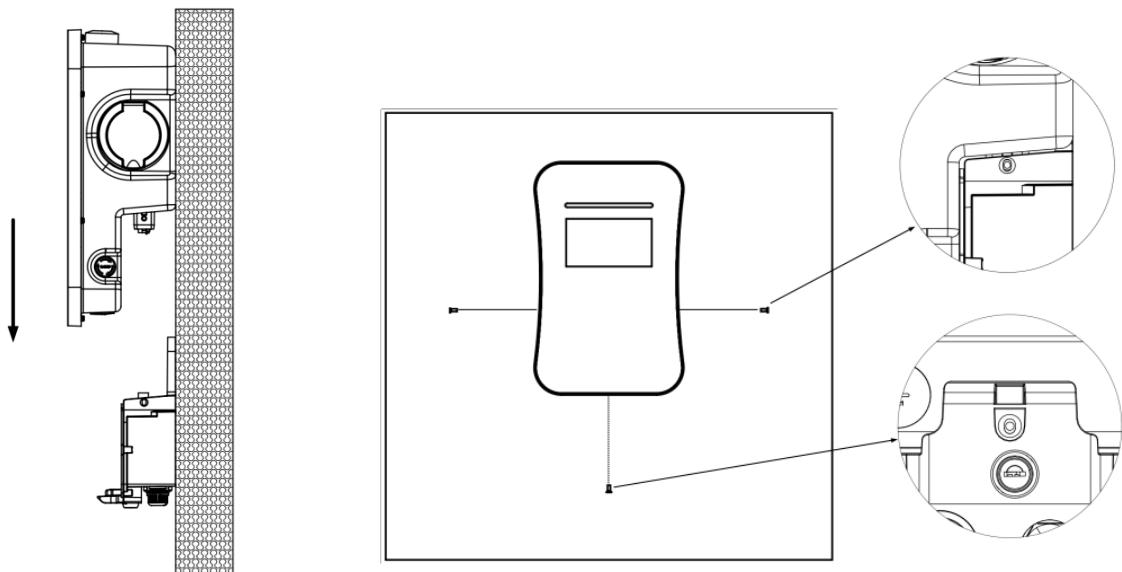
Installation der Wallbox (exemplarisch DaheimLader Touch Pro dargestellt)
